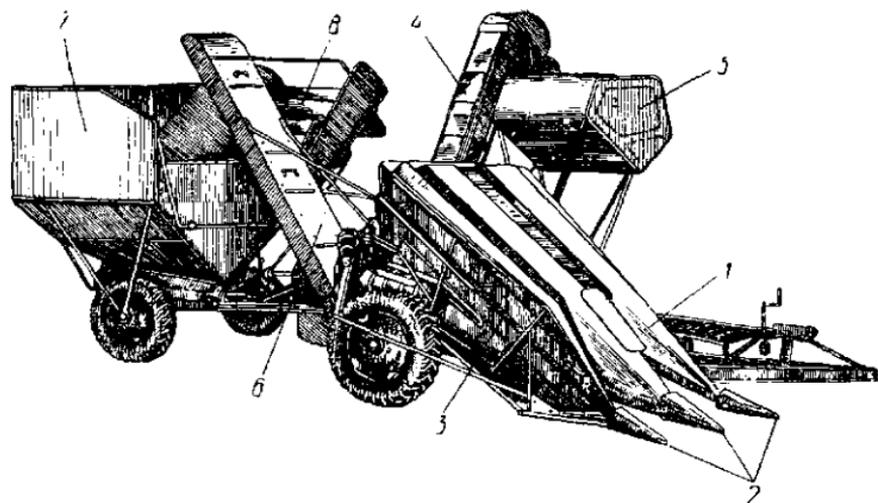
Кукурузоуборочный комбайн КУ-2:
